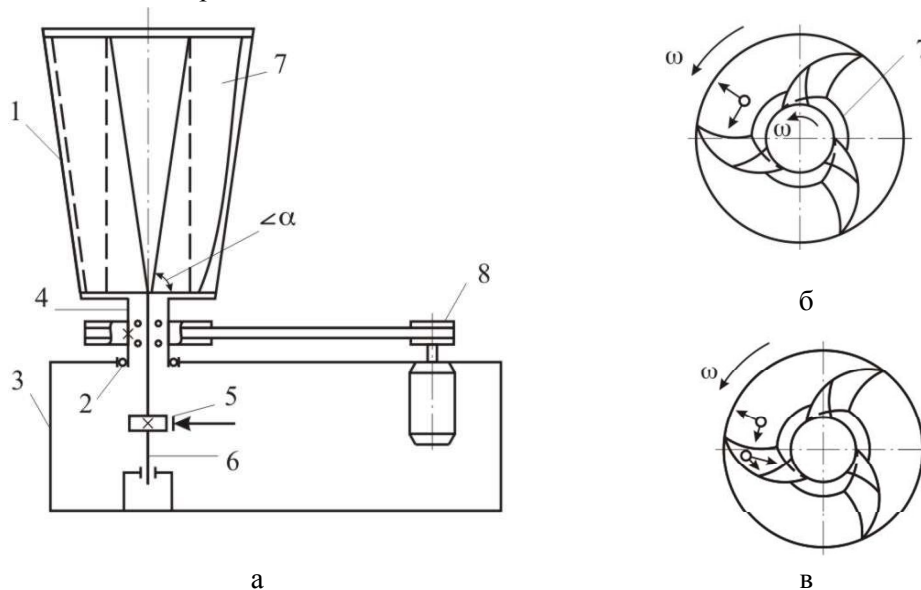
Схема установки для відцентрової обробки деталей; а – схема, б - контейнер для періоду спільного обертання контейнера і завихрювача, вид зверху; в - контейнер у момент зупинки завихрювача, вид зверху: 1 – контейнер, 2 – підшипниковий вузол, 3 – основа, 4 - маточина, 5 - керований гальмівний механізм, 6 – вал, 7 – завихрювач, 8 – привод.
